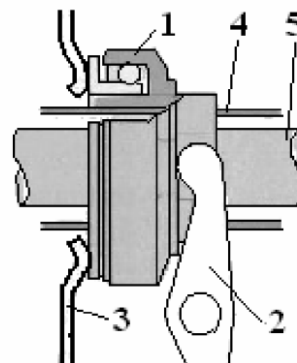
Муфта выключения сцепления с упорным шариковым подшипником:
